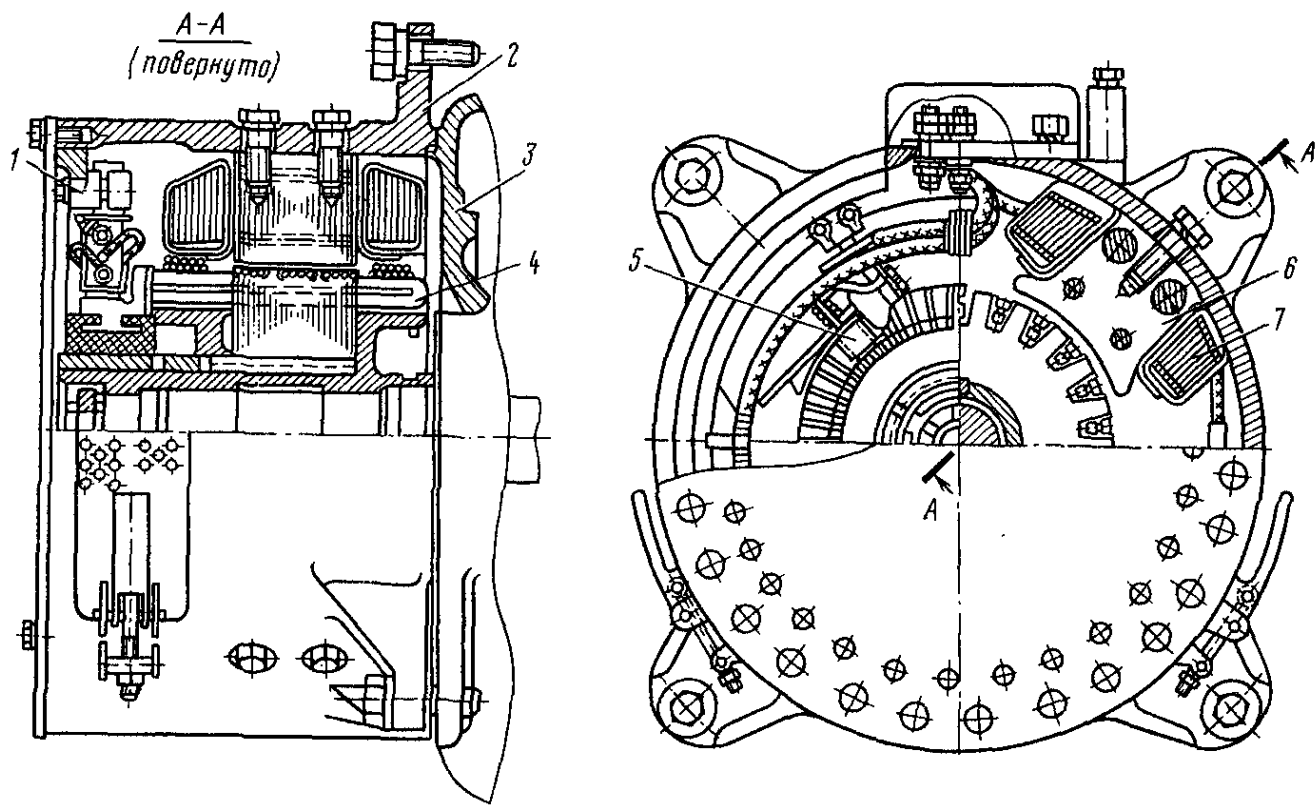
Продольный и поперечный разрезы генератора управления ДК-405К:
